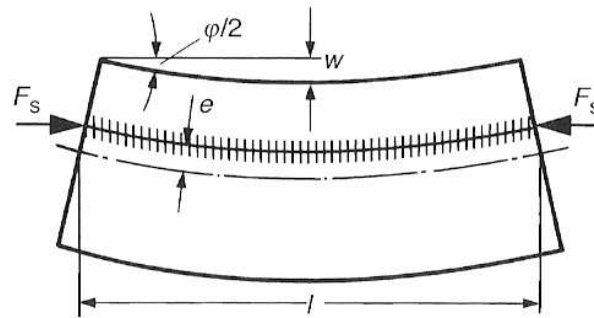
Doblado longitudinal de una placa con soldadura excéntrica ¹¹
